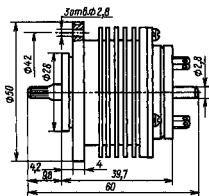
12 Габаритные и установочные размеры двигателя МГ-1,5
